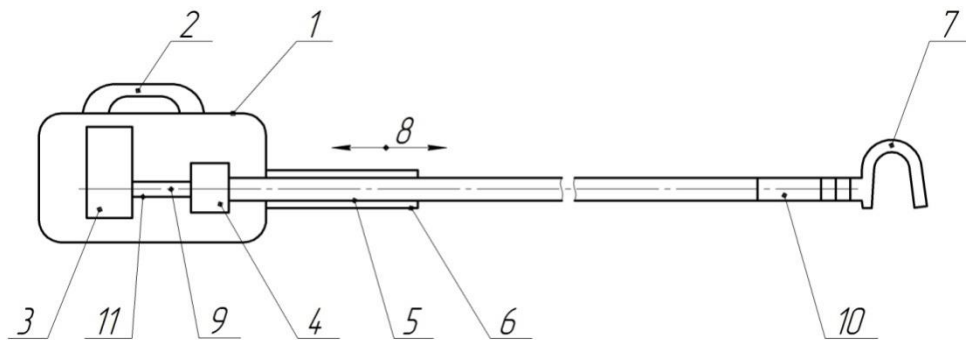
Схема ручного віброударного струшувача плодів:
